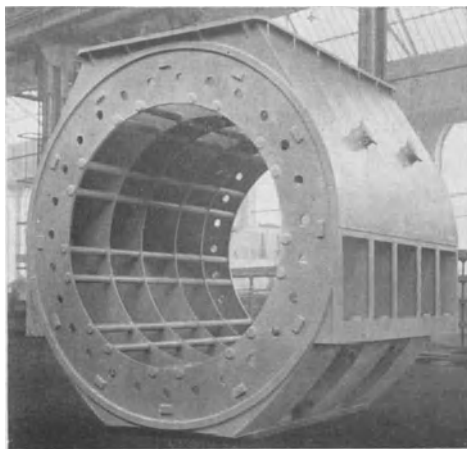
Geschweißtes Dynamogehäuse.
